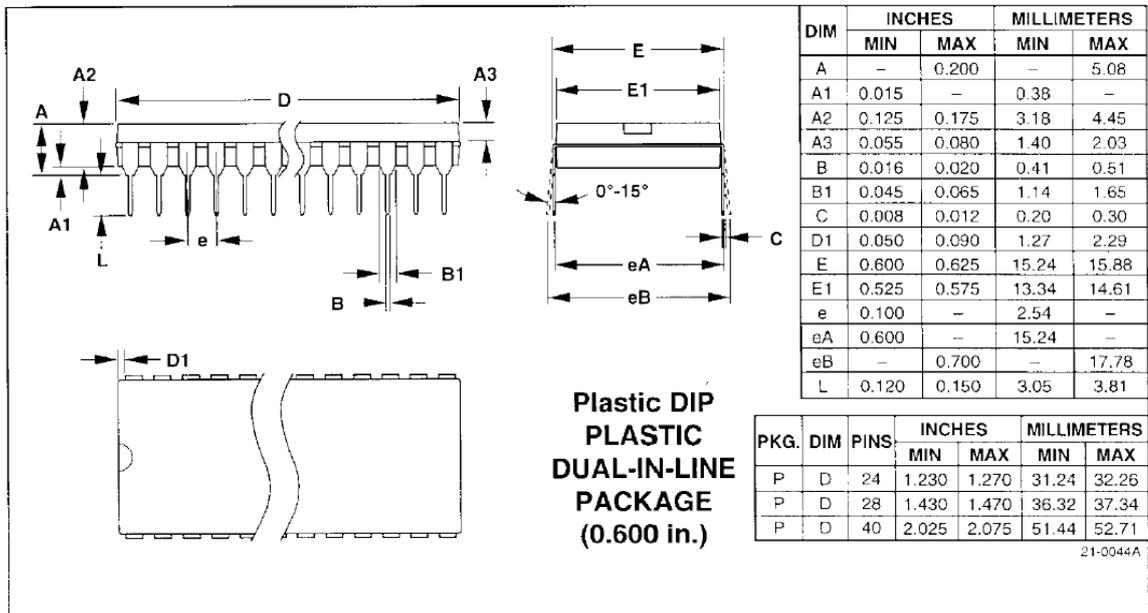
Exemplo de dimensões de um circuito integrado com encapsulamento DIL40, padrão 600 mils.
